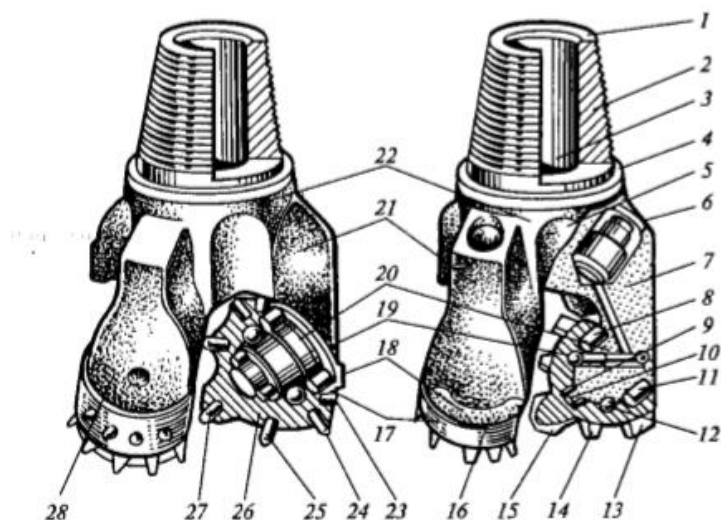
Трехшарошечное долото: 1 – торец присоединительного ниппеля; 2 — присоединительный ниппель с замковой резьбой; 3 — внутренняя полость присоединительного ниппеля; 4 — упорный уступ долота; 5 — резервуар для размещения смазки; 6 — система компенсации давления смазочного материала; 7 — лапа; 8 — периферийный роликовый радиальный подшипник качения; 9 — концевой радиальный подшипник скольжения; 10— концевой упорный подшипник скольжения; 11 — герметизирующий элемент; 12 — средний шариковый радиально-упорный подшипник качения; 13 — фрезерованный зуб периферийного венца; 14 — фрезерованный зуб среднего венца; 15 — фрезерованный зуб вершины шарошки; 16 — наплавка зерновым твердым сплавом; 17 — шарошка; 18 — козырек лапы; 19 — замковый палец; 20 — цапфа лапы; 21 — спинка лапы; 22 — корпус долота; 23 — твердосплавный зубок, запрессованный в тыльный корпус шарошки; 24 — твердосплавный зубок периферийного венца шарошки; 25 — твердосплавный зубок среднего венца шарошки; 26— концевой роликовый подшипник скольжения; 27 — твердосплавный зубок вершины шарошки; 28 — твердосплавный зубок, запрессованный в козырек лапы
